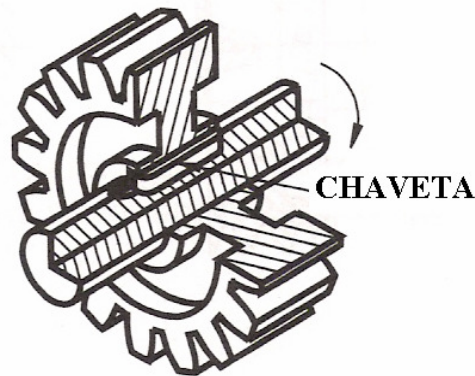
Engrenagem fixada ao eixo com chaveta
